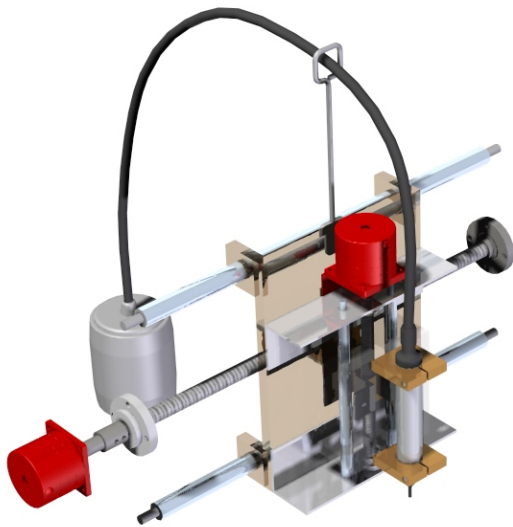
Mecanismo de posicionamiento del eje Z con el motor de la herramienta de corte instalado sobre el mecanismo de posicionamiento del puente fijo (eje X).
